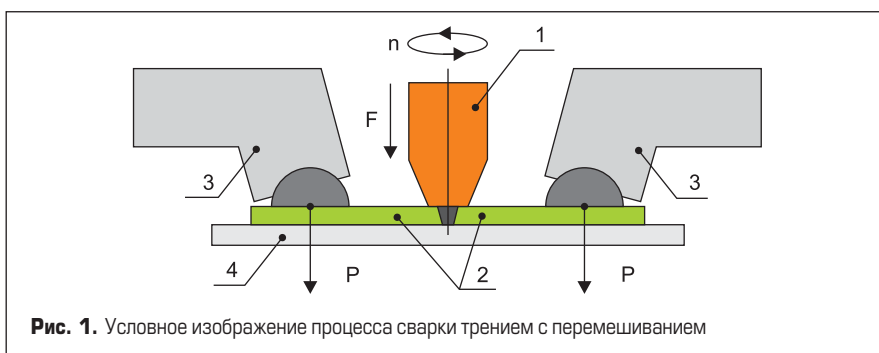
Условное изображение процесса сварки трением с перемешиванием
